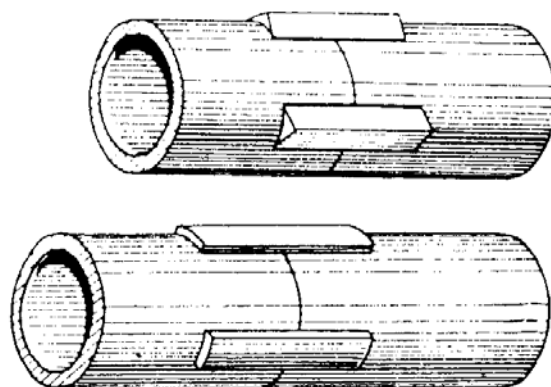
Усилительные планки из полосовой и угловой стали, привариваемые на ослабленный сварной стык
